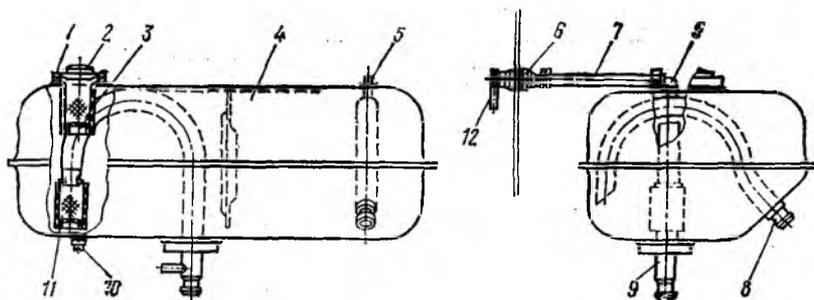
Конструктивная схема бака рабочей жидкости погрузчика 4043М:
